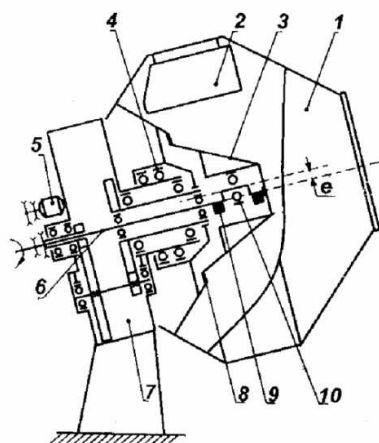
Кинематическая схема экспериментального вибрационного смесителя гравитационного типа: 1 – смесительный барабан; 2 – лопасти; 3 – корпус вибровозбудителя; 4 – подшипники; 5 – электродвигатель привода вращения барабана; 6 – эксцентриковый вал; 7 – двухступенчатый редуктор; 8 – резиновая муфта; 9 – противовесы; 10 – шатунный подшипник
